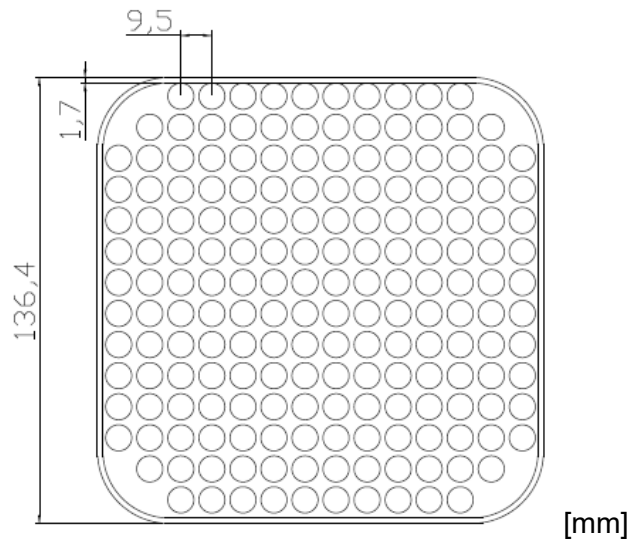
Esquema da usinagem de furos, vista superior do corpo de prova.
